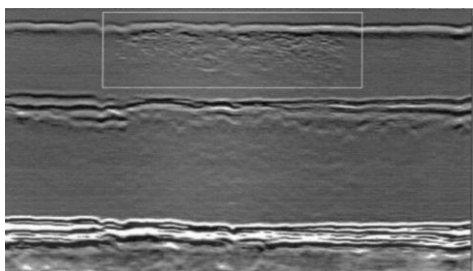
Скопление газовых пор в сварном шве
